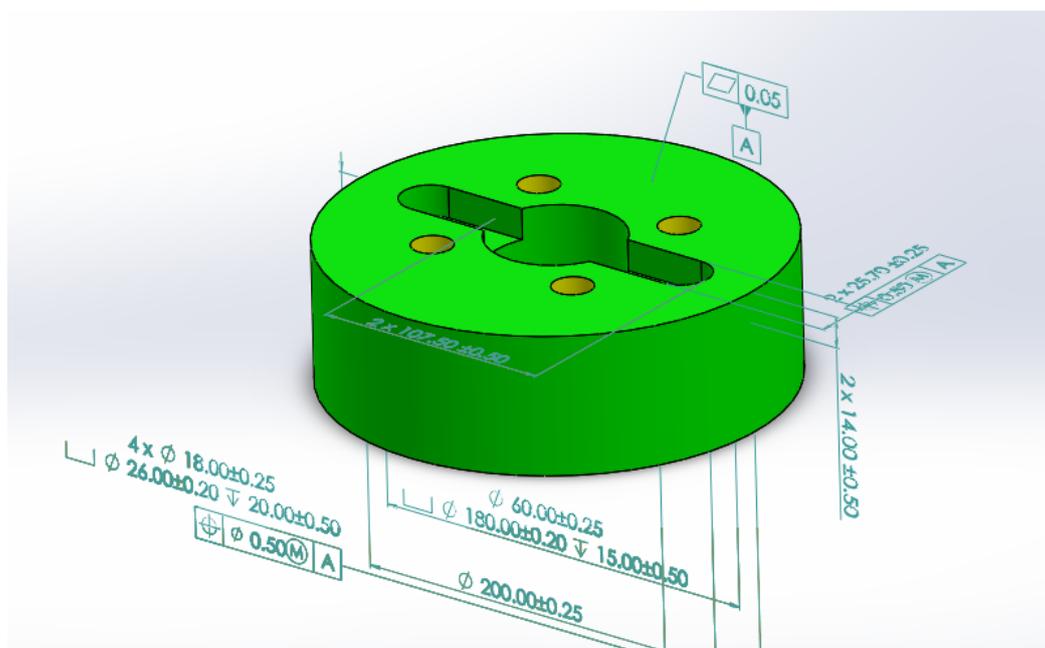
Exemplo de componente dimensionado e toleranciado utilizando o modo automático do *DimXpert
